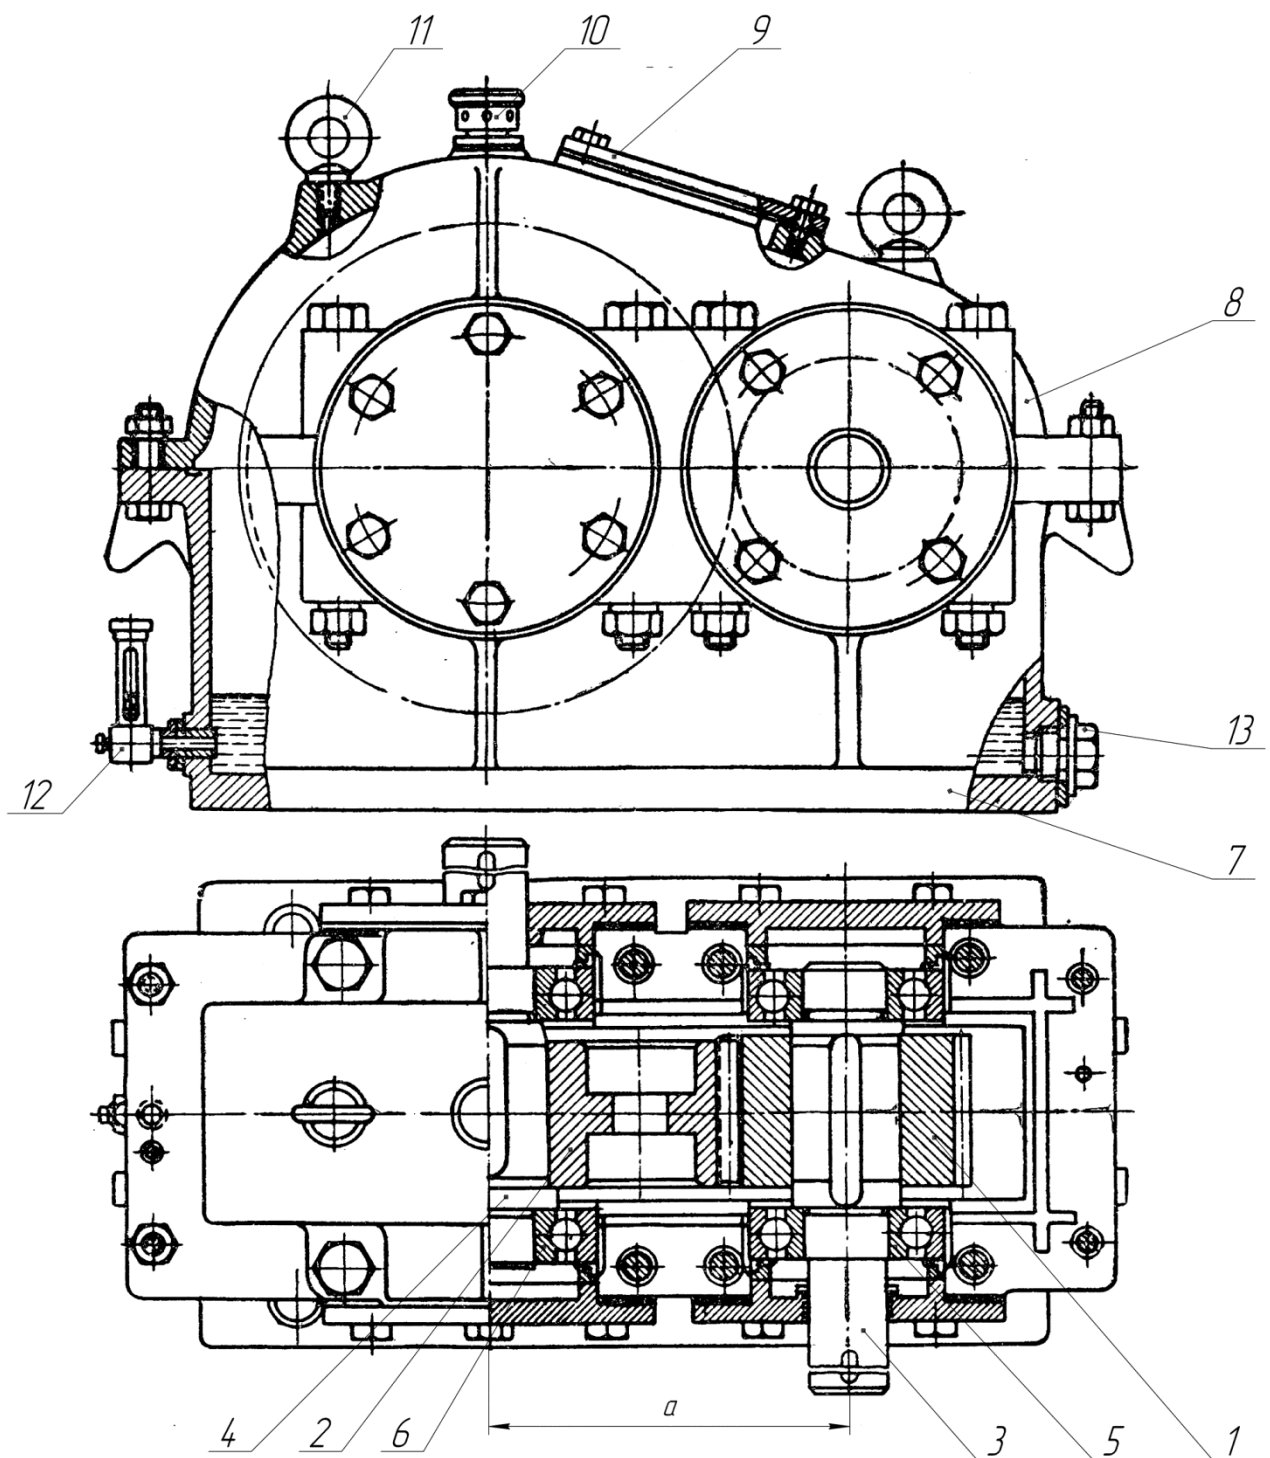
Цилиндрический одноступенчатый зубчатый редуктор.
